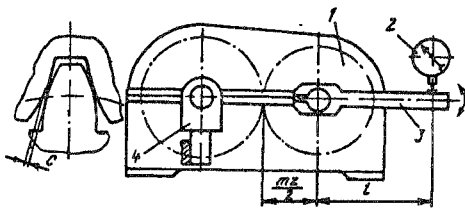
Схема контроля бокового зазора в зацеплении пары зубчатых колес
